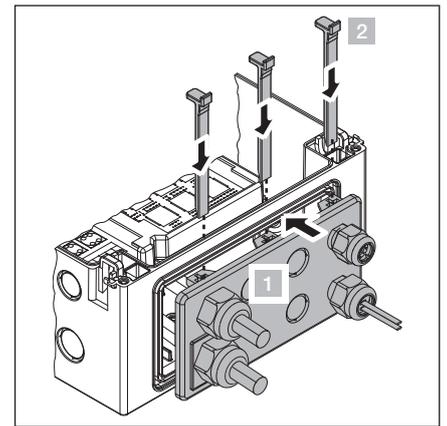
Einbau der Verschraubungsflanschplatte
